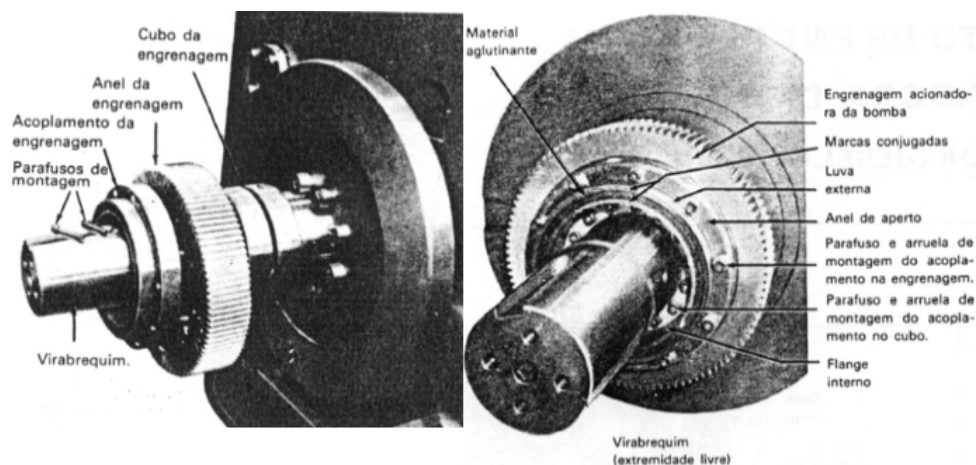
Conjunto de engrenagens acionadoras da bomba [8]
